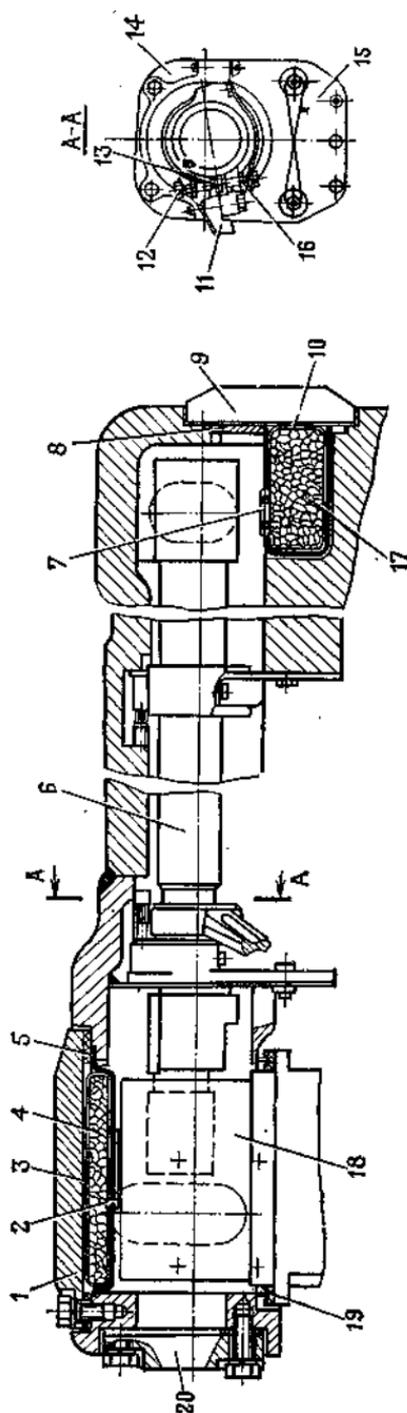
Установка головки прицела-дальномера и базовой трубы в машине:
